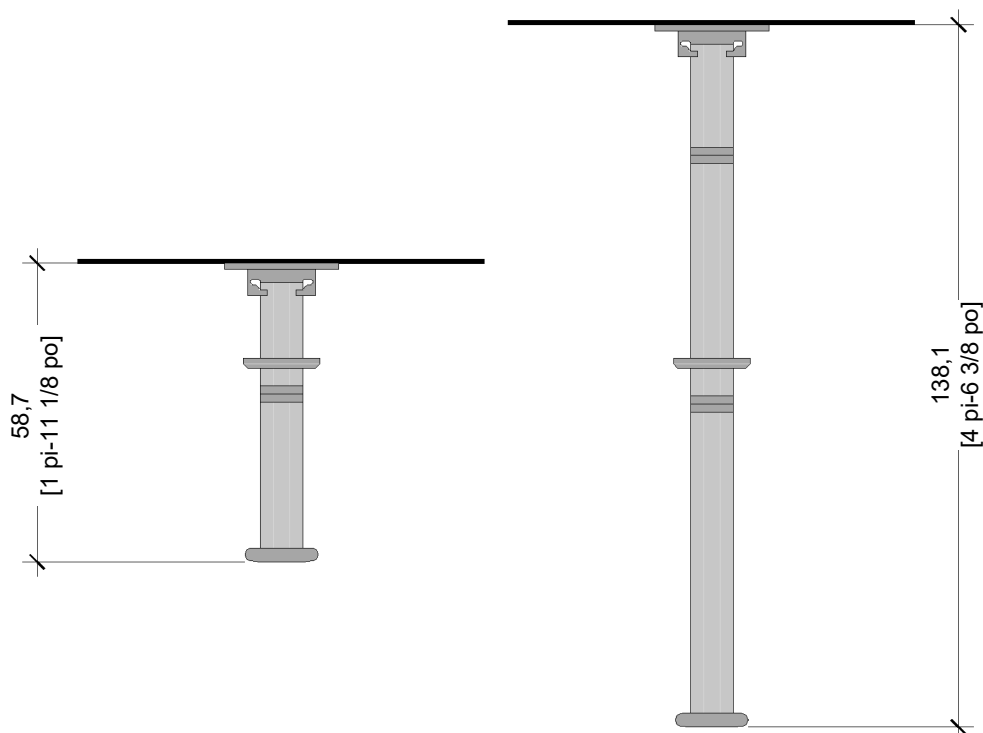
Vue en section de la plaque de montage au plafond et du montant
